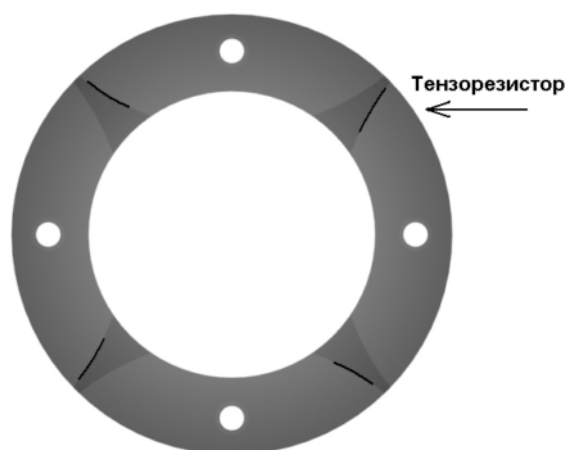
Схема установки тензорезисторов на прорези корпуса правой полумуфты
